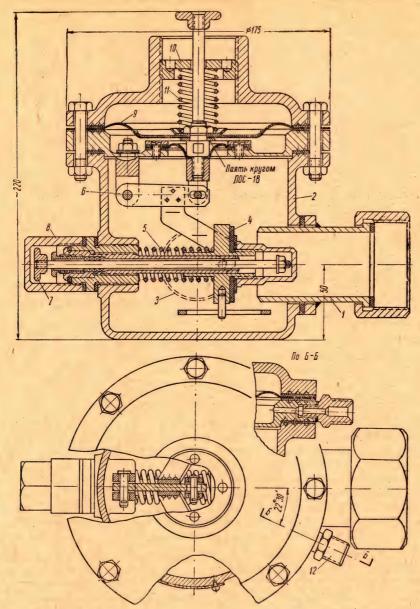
Предохранительный запорный клапан типа $\Pi 3 K_H$ -50: 1 — выходной штуцер $\varnothing 2^{\prime\prime}$; 2 — корпус клапана; 3 — входной штуцер $\varnothing 1.5^{\prime\prime}$; 4 — запорный клапана; 5 — пружина для установки клапана; 6 — рычажный провод; 7 — головка для установки клапана; 8 — предохранительный колпак; 9 — мембрана клапана; 10 — тайка для настройки клапана; 11 — пружина для настройки клапана; 12 — ниппель для подвода импульса регулируемого давле-
